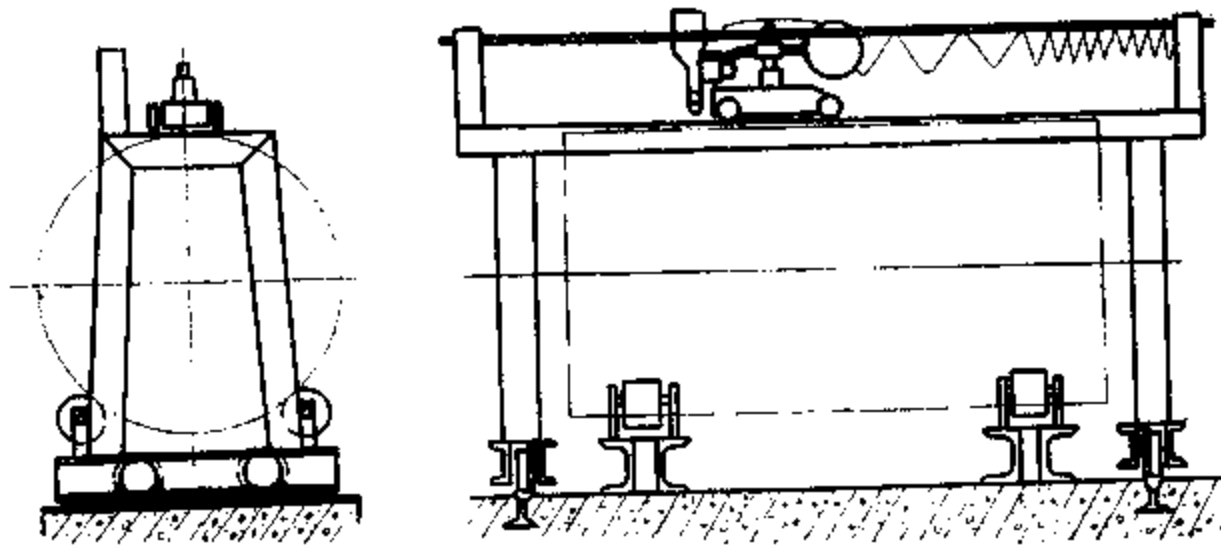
门式焊接架上焊接圆筒纵缝
